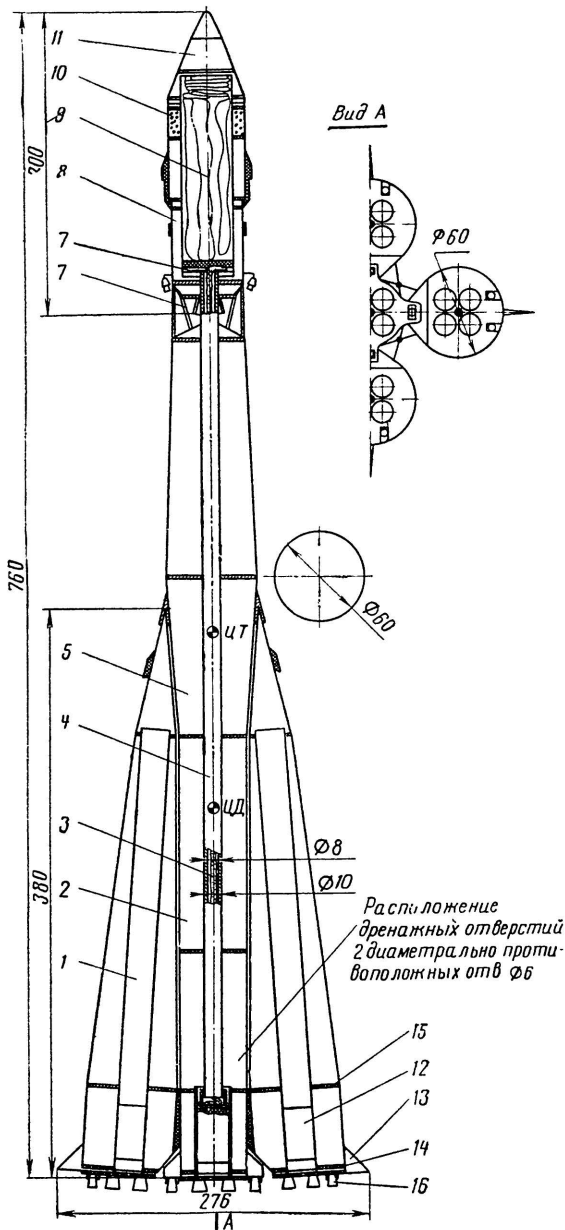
Компонка модели ракеты-носителя космического корабля «Восток»: 1 — боковой ускоритель первой ступени; 2 — центральный блок второй ступени; 3 — нитка стопина; 4 — центральная силовая труба; 5 — конус центрального блока; 7 — ферма; 8 — корпус третьей ступени; 9 — парашют системы спасения модели; 10 — загрузка; 11 — головной обтекатель; 12 — микро-РДТТ первой ступени; 13 — стабилизатор; 14, 15 — шпангоуты бокового ускорителя; 16 — рулевое сопло; 17 — пороховая навеска системы спасения
